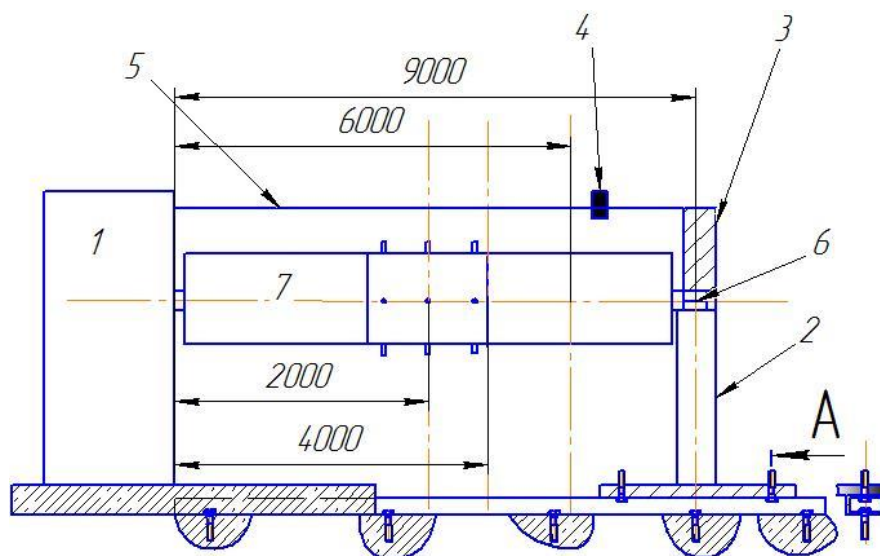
Стенд для контроля качества ремонта и балансировки длиномерных шнеков зерноуборочных комбайнов: 1 – основание; 2 - передвижная стойка; 3 - инструментально - измерительный комплекс; 4 - датчик расстояния; 5 – брус; 6 – опоры; 7 - шнек
